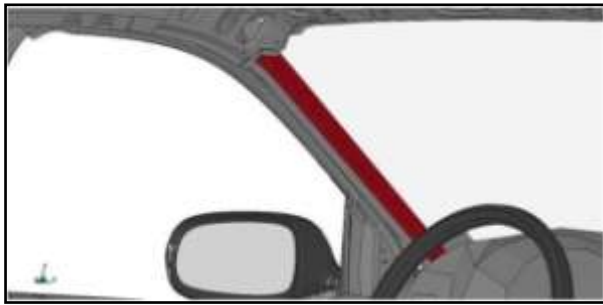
Detail konstrukce tvaru–U (10)
